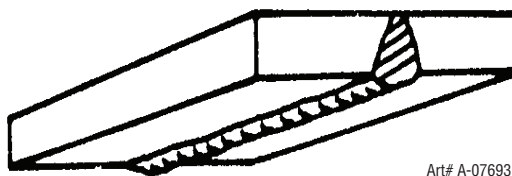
Position au plafond, Soudure bout à bout
